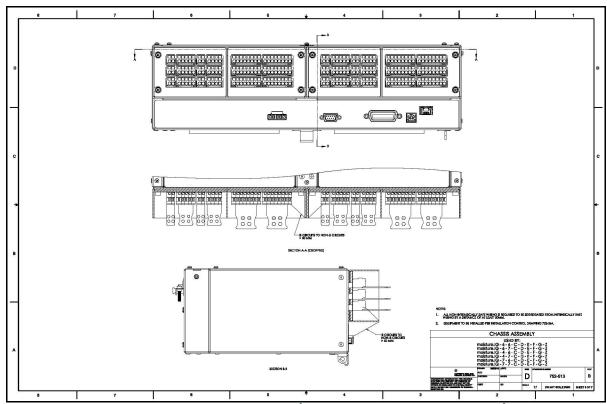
Conjunto de chassis (desenho 752-513\_revB, SH 5 de 5)
